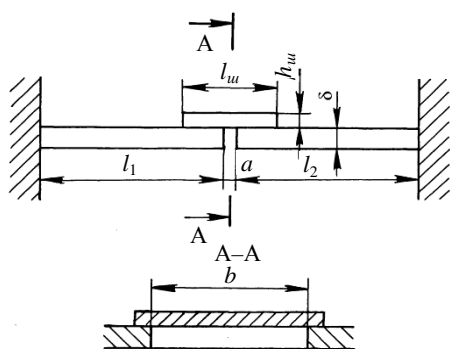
Схема сварного соединения при устранении трещины
